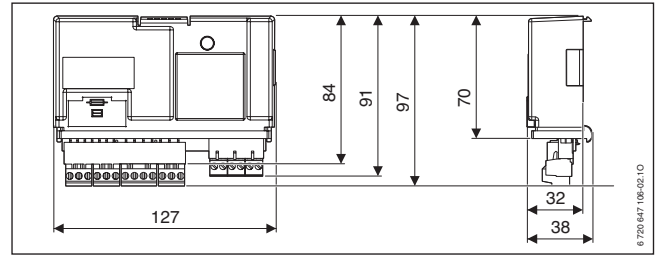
Abmessungen Mischmodul MM50/SM50 bei Einbau in den Wärmereizer (Maße in mm)
